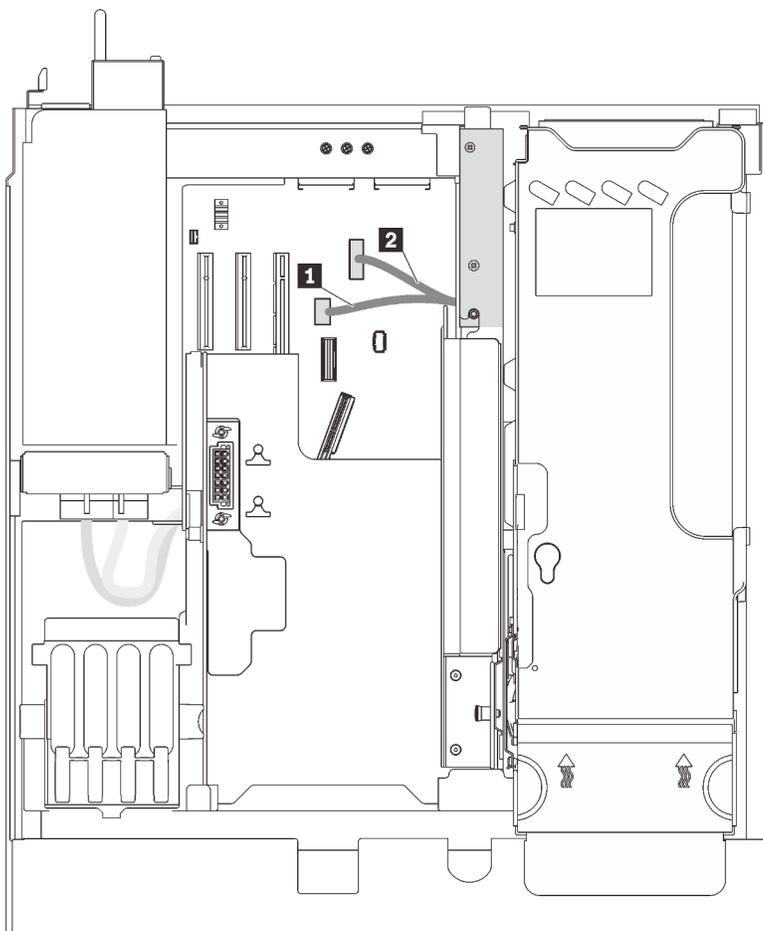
Instradamento dei cavi del telaio unità da 7 mm
